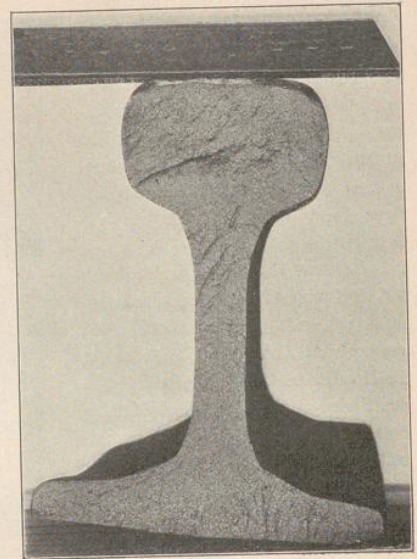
Eisen. Gufsstück einer Eisenbahnschiene von weichem Bessemerstahl (Flussstahl) mit feinem, gleichmäßigem Korne.
